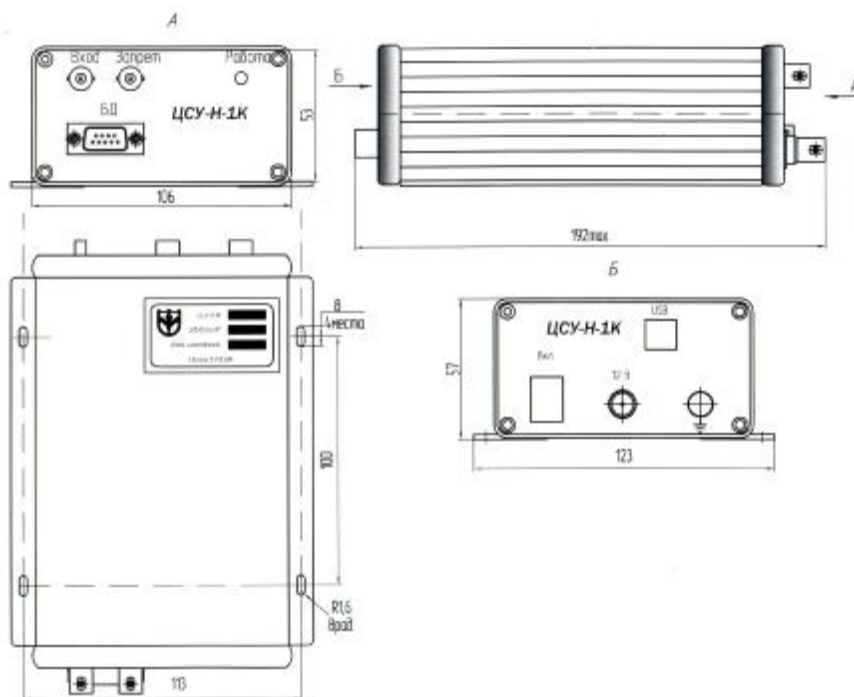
Габаритно-присоединительный чертеж ЦСУ-1К.
